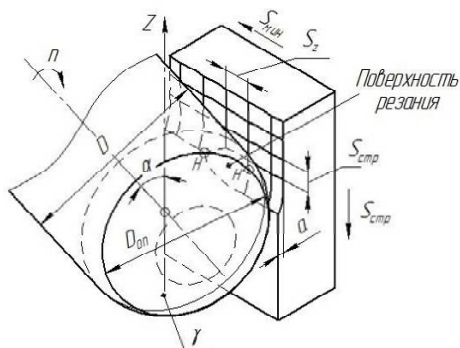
Схема финишного фрезерования ТЭ детали тороидальной концевой фрезой:
